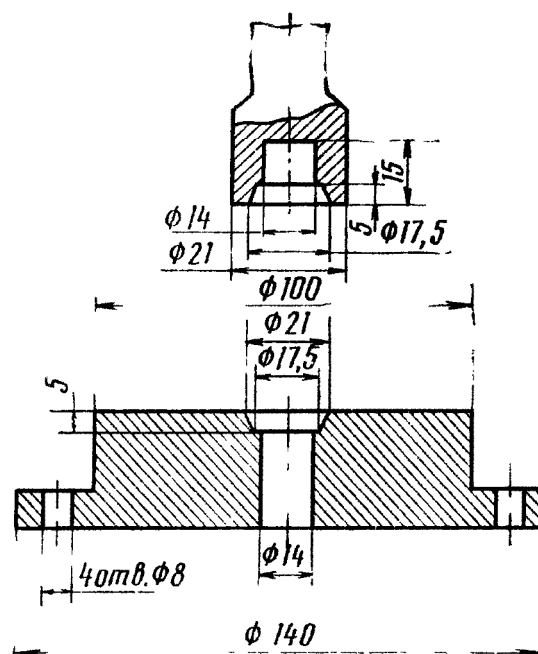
Приспособление для обжатия шарнира тяг стеклоочистителя
